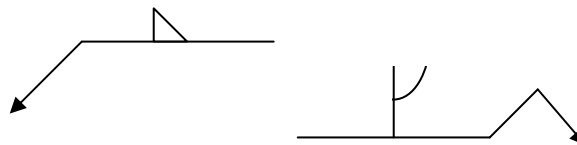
Orientación de símbolos de tipos de soldadura
